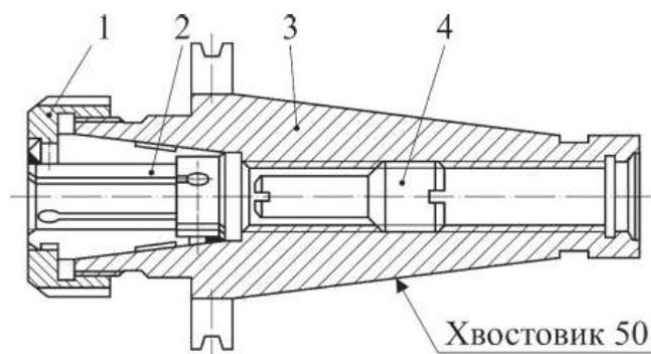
Патрон для кріплення кінцевих фрез:
